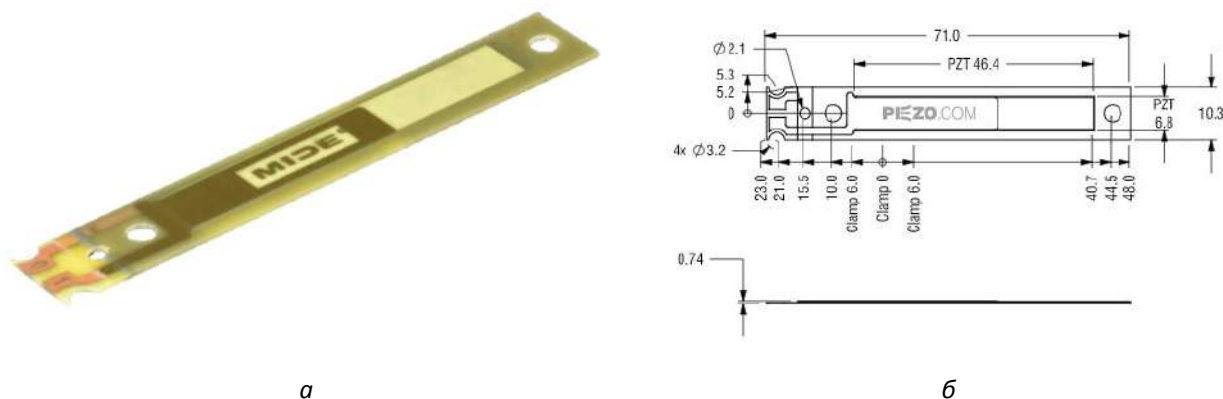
Пьезоэлемент S129-H5FR-1803YB: а – общий вид пластины; б – геометрические параметры
